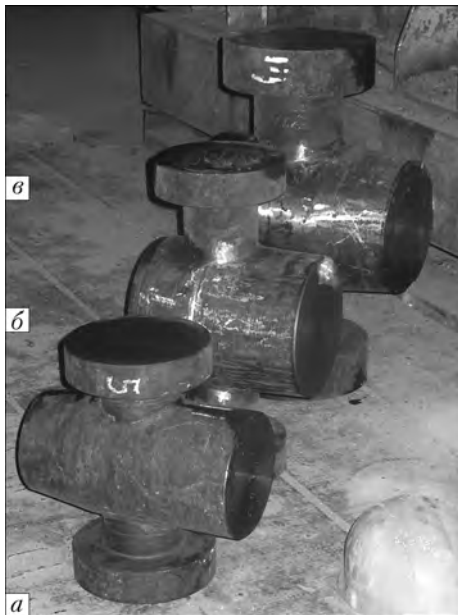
Внешний вид заготовок корпусов фланцевых задвижек, полученных способом ЭШЛ с приплавлением: а – Ду-65 на давление 35 МПа; б – Ду-50 на давление 70 МПа; в – Ду-80 на давление 70 МПа
